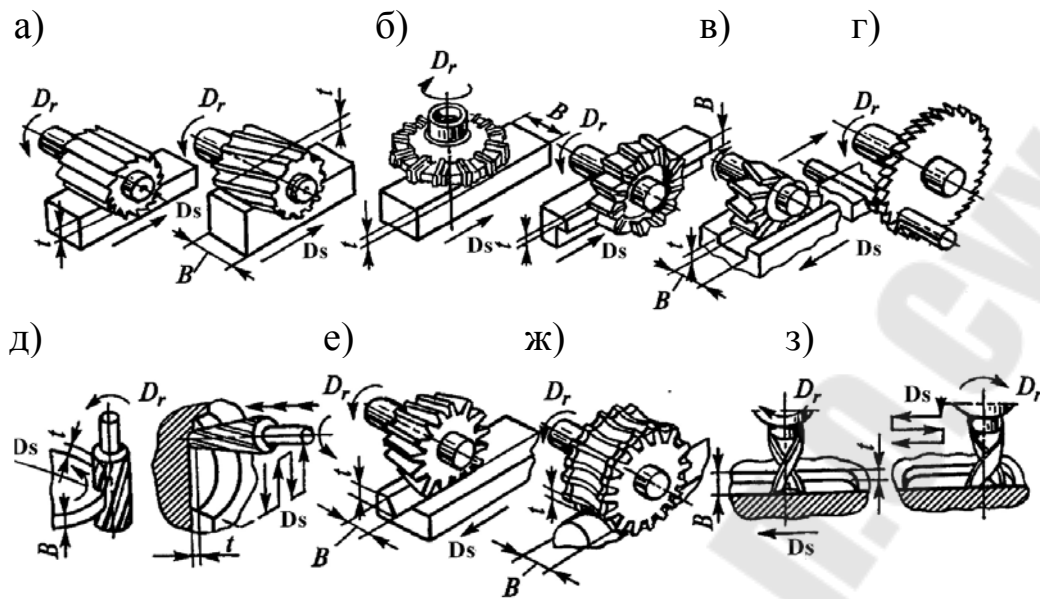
Виды работ, выполняемых фрезерованием, и применяемые фрезы:
